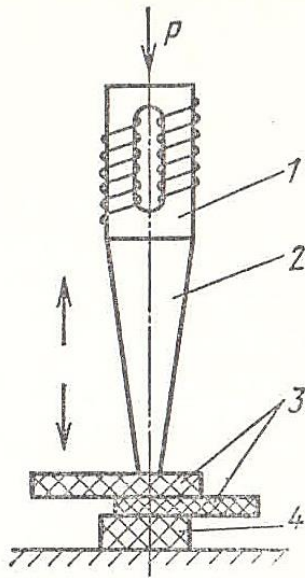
Схема ультразвукового зварювання пластмас:
